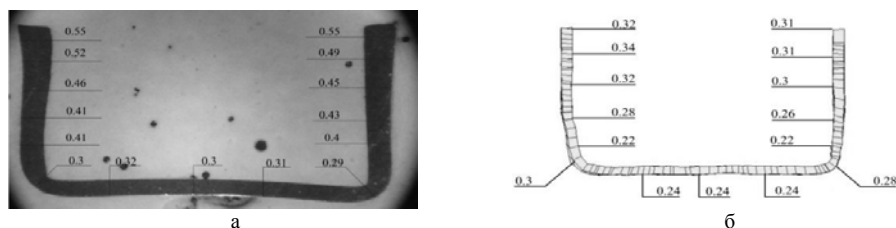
Продольный разрез полой цилиндрической детали из алюминиевого сплава АД1М:
